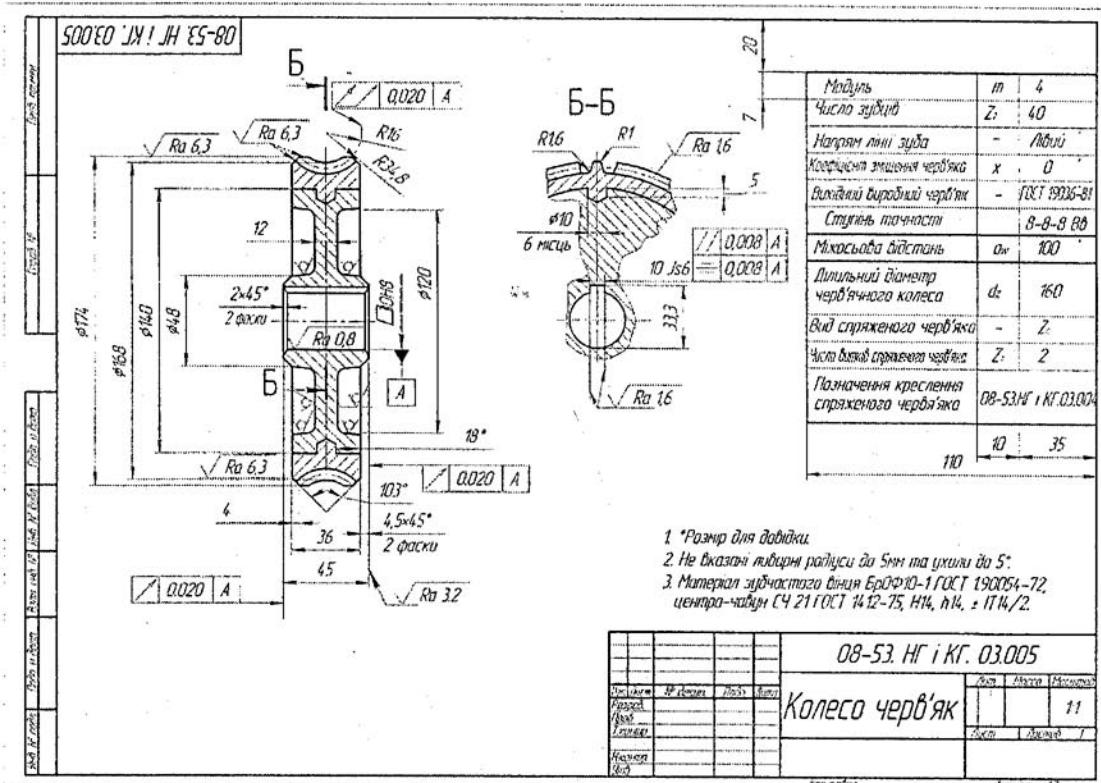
Робочий кресленик черв'ячного колеса (*worm gear*)
